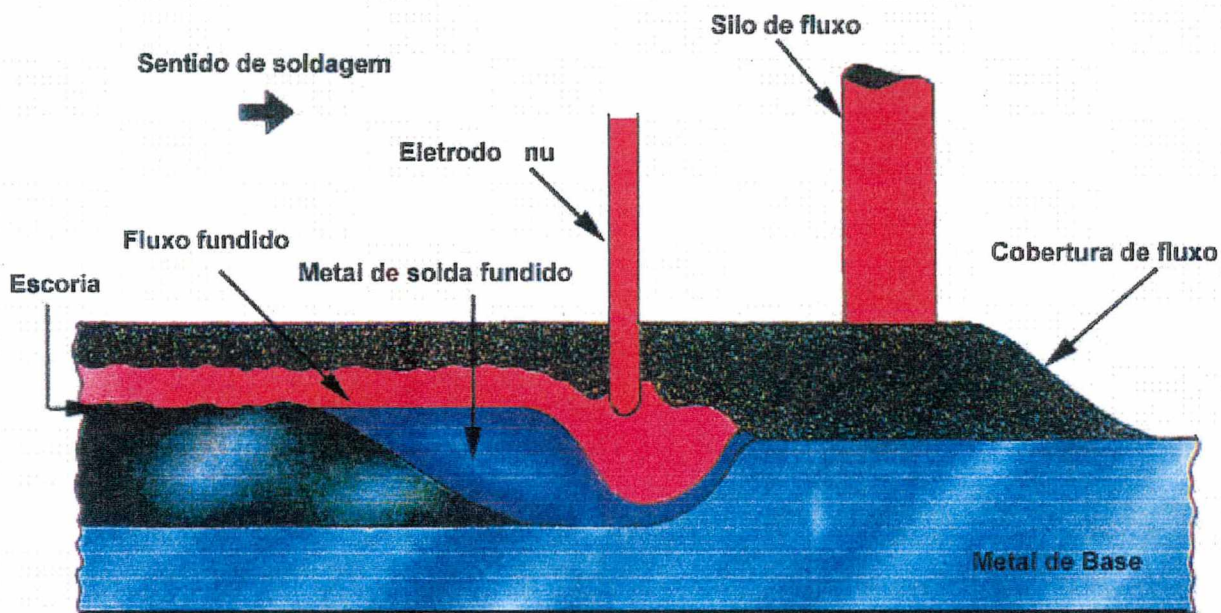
Representação esquemática do processo de soldagem a arco submerso.
